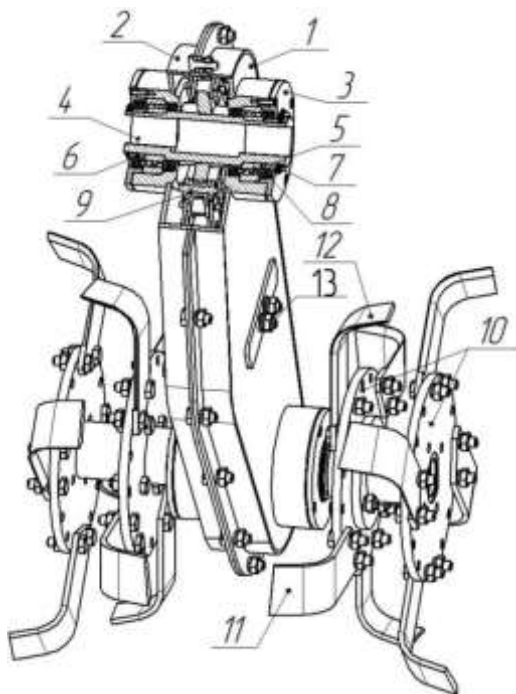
Редуктор КФ 04.000 в сборе с лопастями
